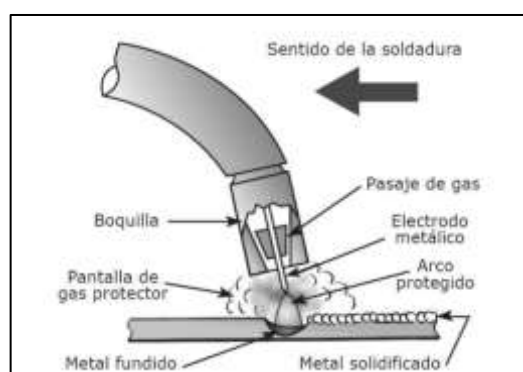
Efectos producidos de una soldadura MIG
